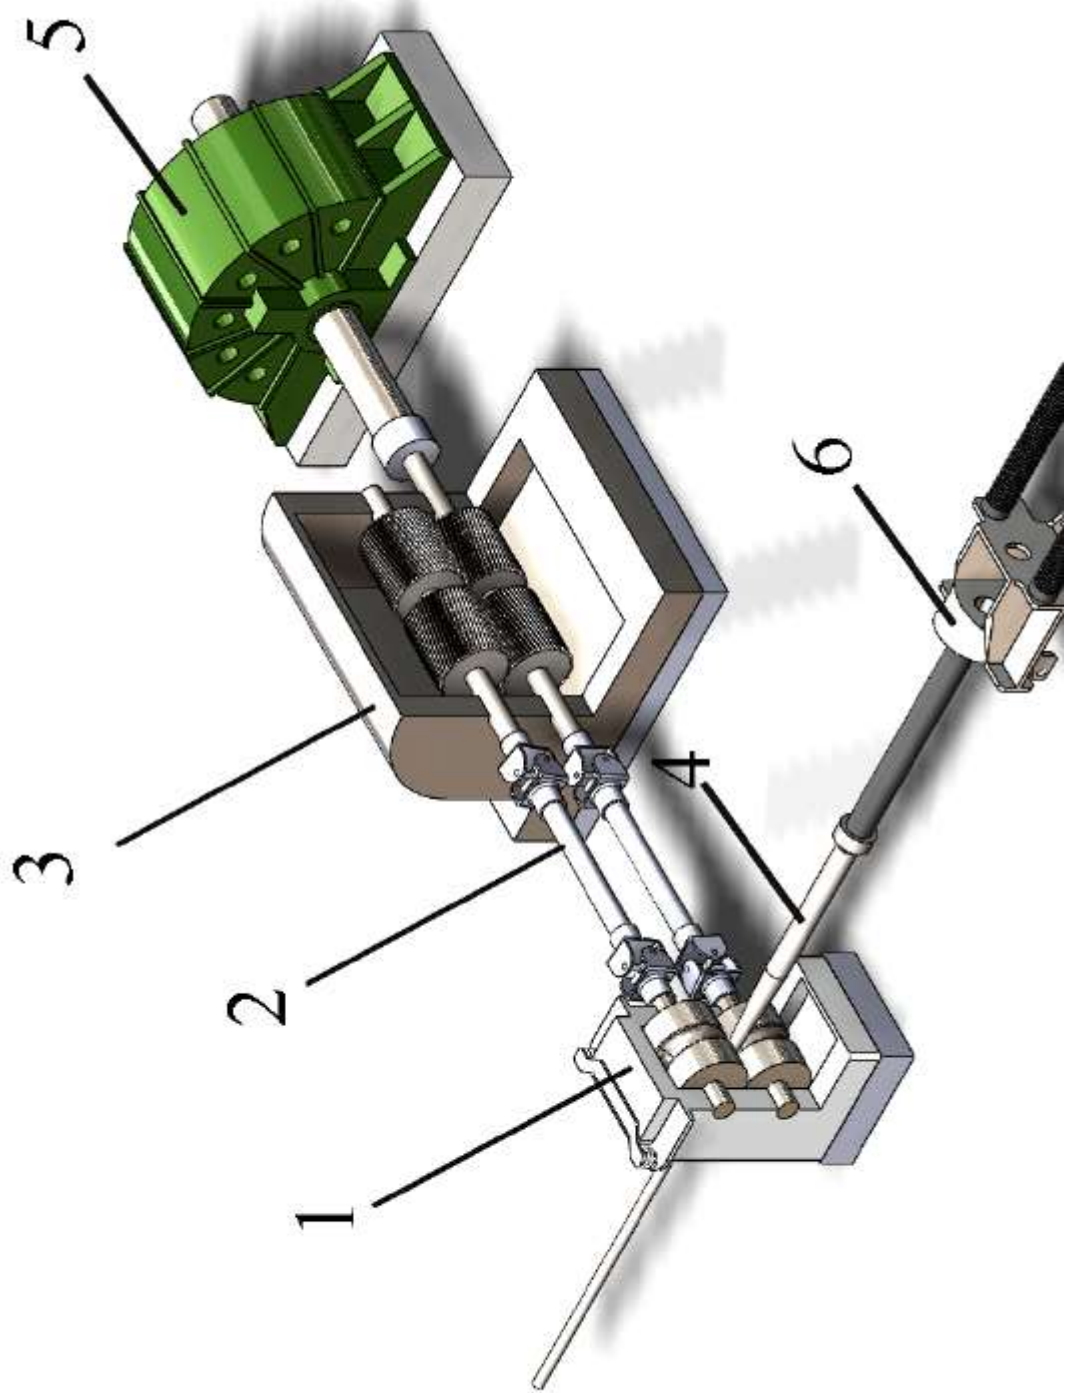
Пильгерстан: 1 – прокатная клеть; 2 – шпиндели; 3 – шестеренная клеть; 4 – трубная заготовка; 5 – двигатель; 6 – вспомогательный механизм
